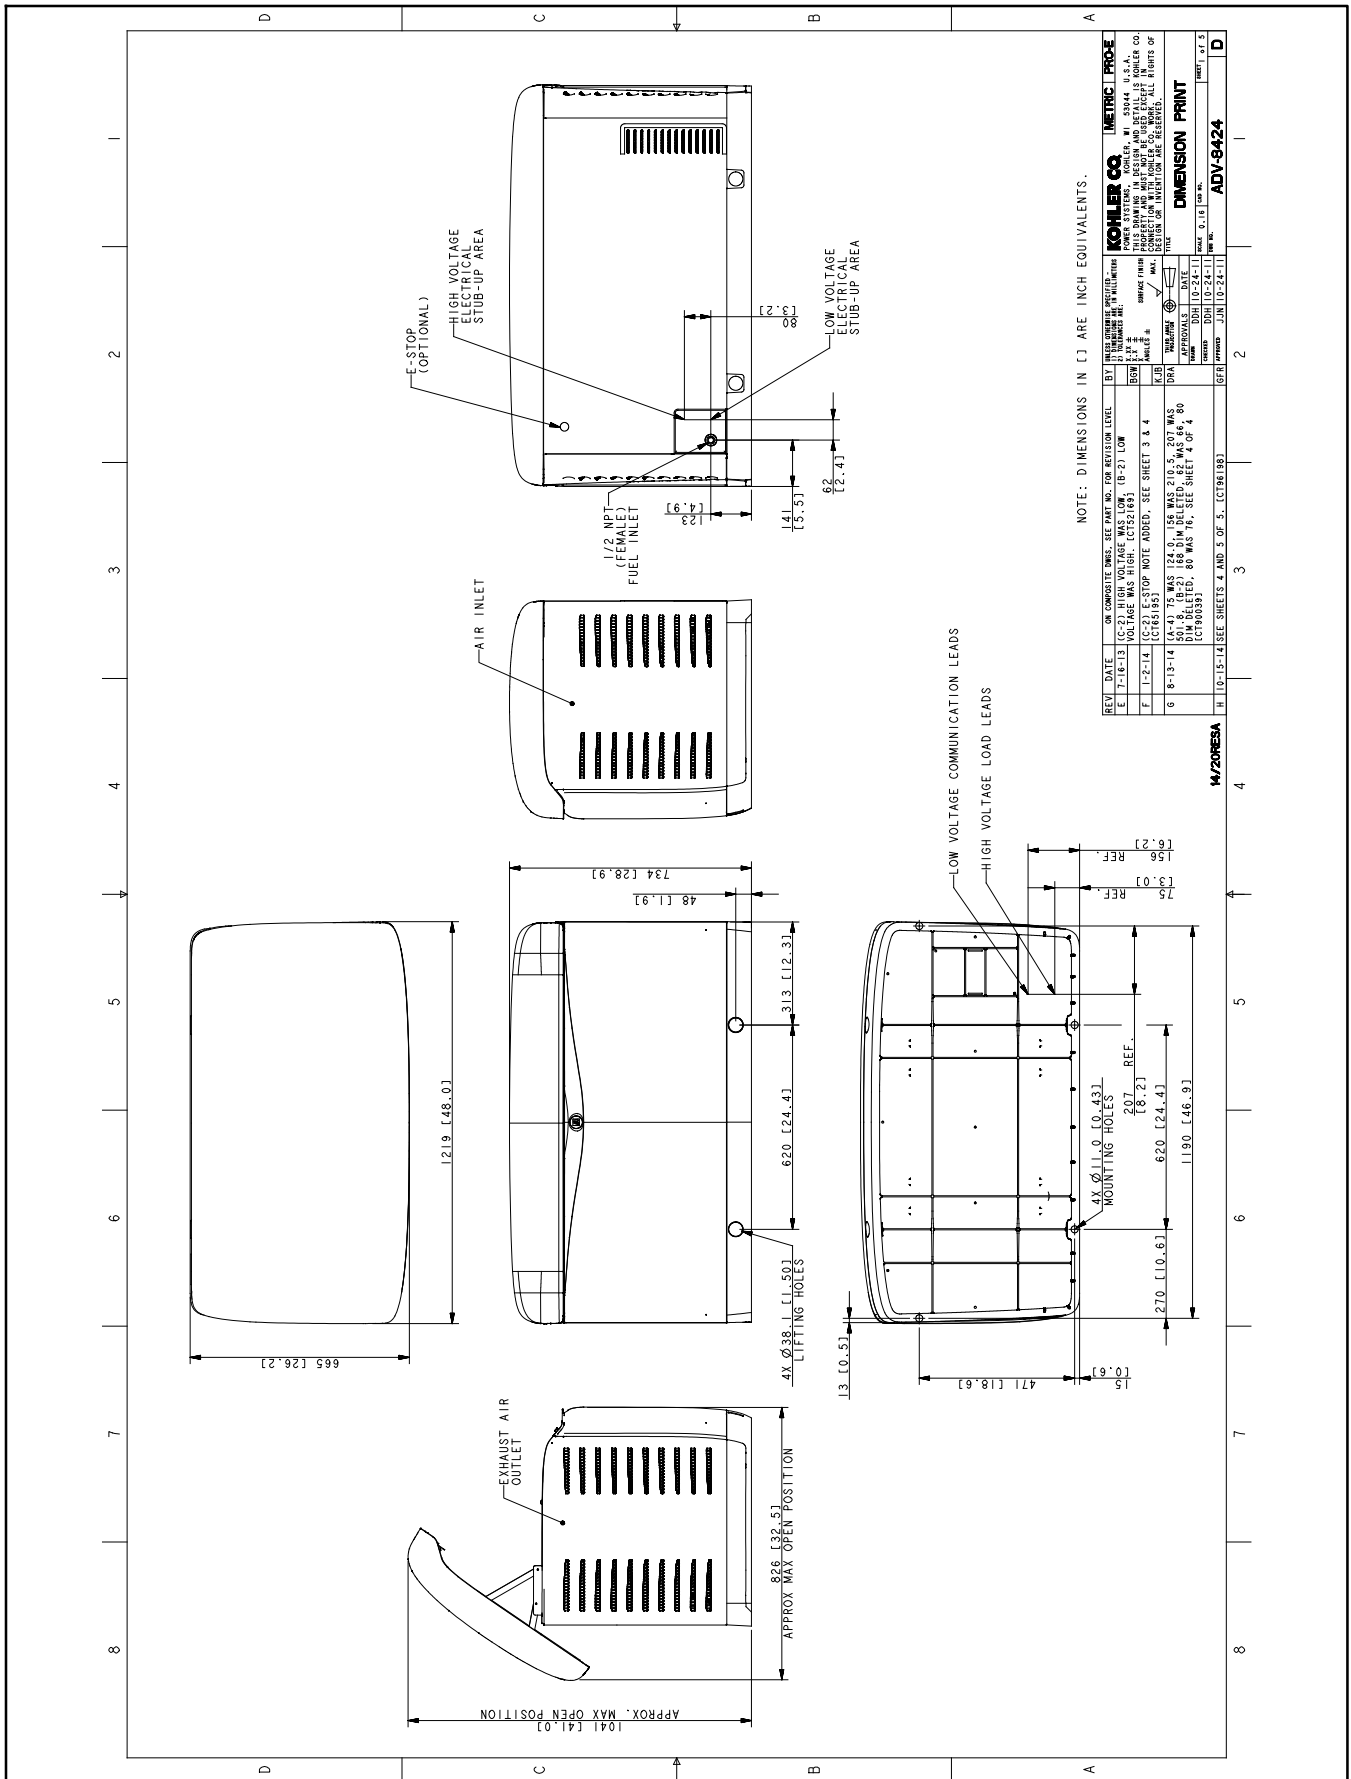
Размерный чертеж ADV-8424, лист 1 из 5
